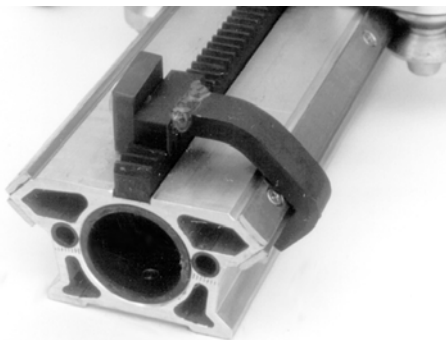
Правильный монтаж направляющей шины на поворотном кронштейне.
